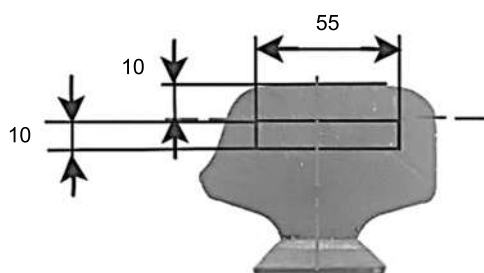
Схема вырезки и размеры образцов для ударных испытаний из головки рельса (мм)
